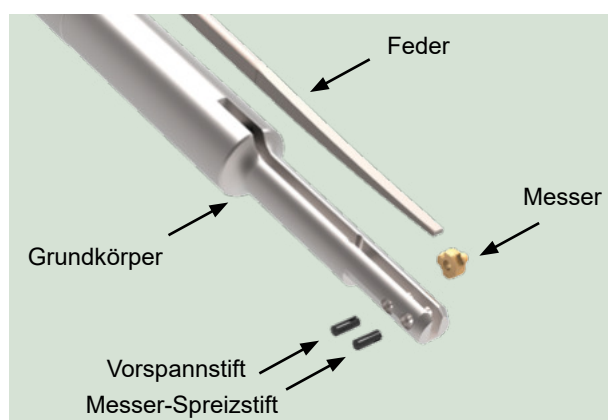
Für den Messerwechsel ist nur der vordere Spreizstift zu entfernen und die Feder auszuschwenken.
